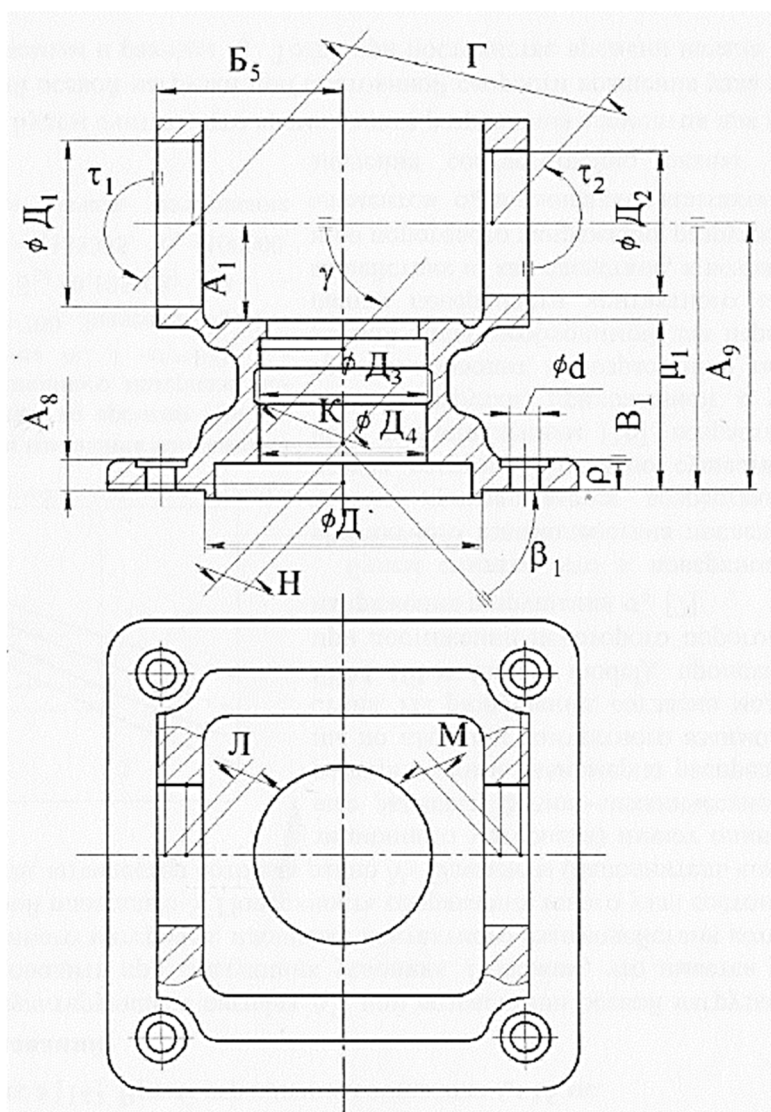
Основні розмірні зв'язки корпусу редуктора
